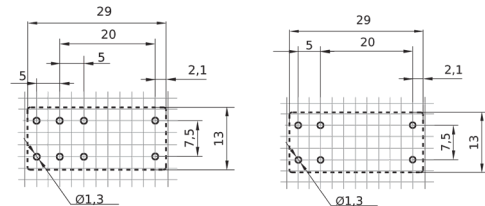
Установочные размеры для печатного монтажа для реле OptiRel G RP40-52 и OptiRel G RP40-61 с CO контактами
